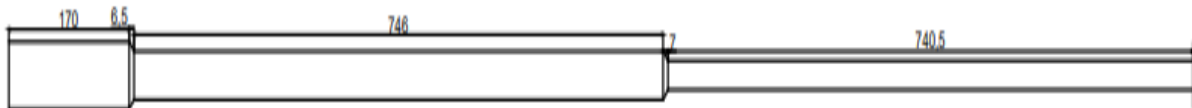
LONGUEUR DE LA POUTRE
